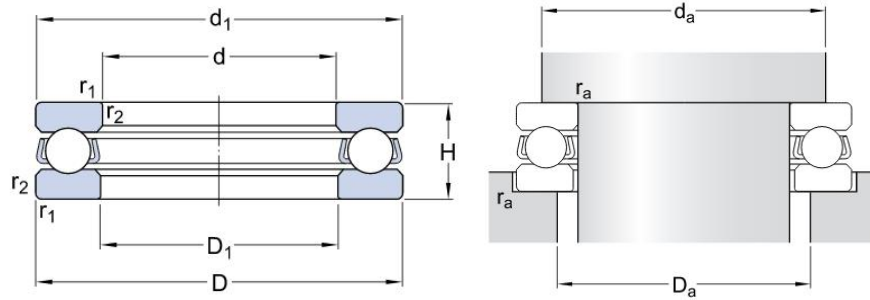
Dimensiones de rodamiento axial 51101 [1].
